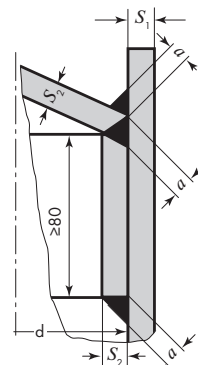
Приварка крышки.  $a = 0,7S_1$
